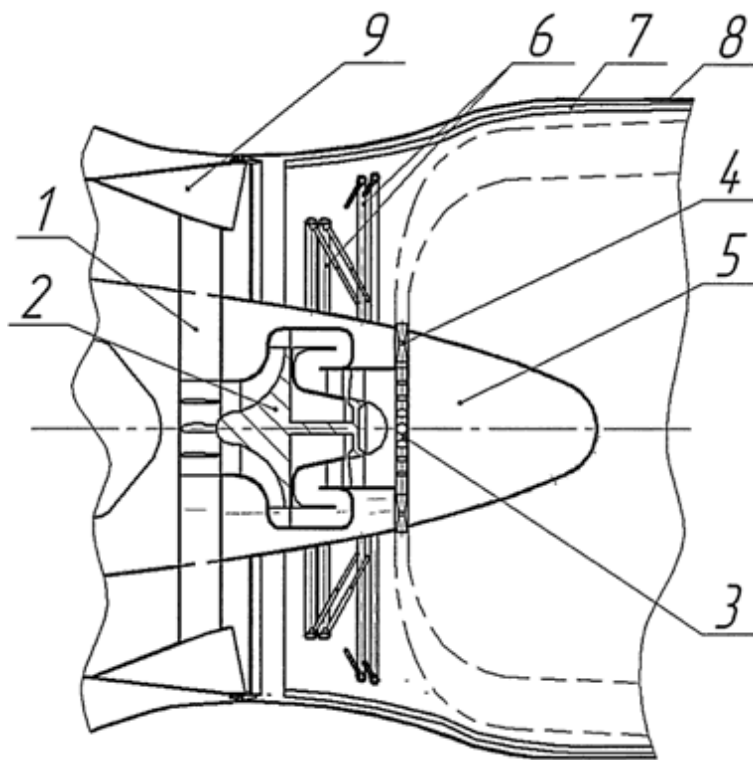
Устройство ФК с газодинамической стабилизацией, где: 1 - патрубки отбора воздуха из второго контура, 2 - малоразмерный газотурбинный двигатель, 3 - пламярассекатель, 4 - система сверхзвуковых сопел, 5 - центральное тело форсажной камеры, 6 - топливные коллекторы, 7 - антивибрационный экран, 8 – корпус ФК, 9 – смеситель.
